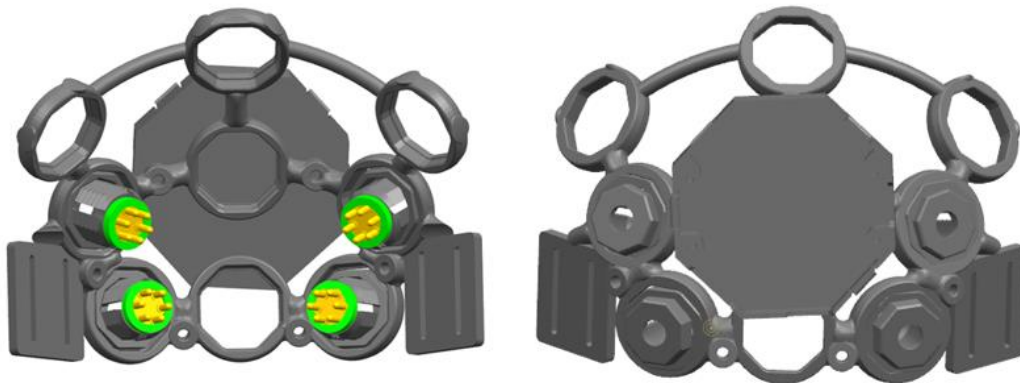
Ensamble del sistema de adquisición, a la izquierda vista frontal, a la derecha vista posterior.
